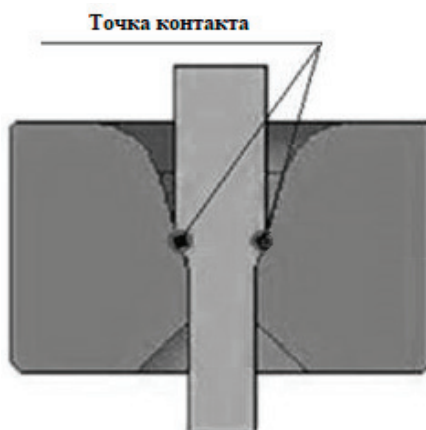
Точка контакта заготовки с поверхностью волоки матрицы
